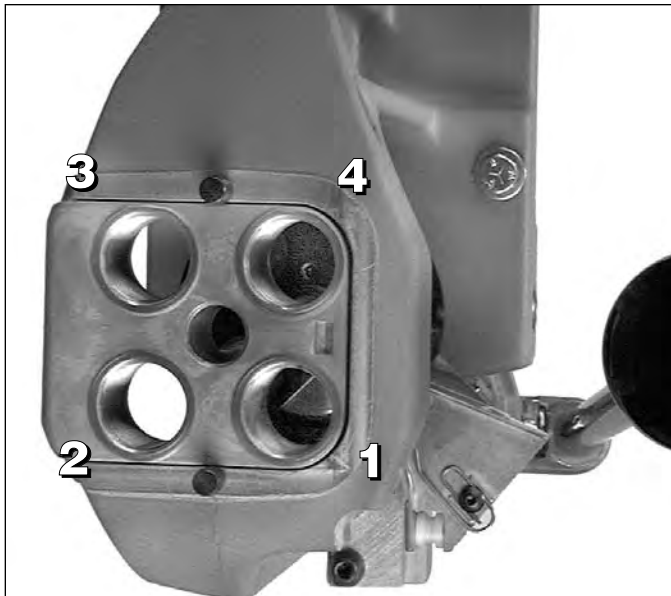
[Figure 11] Werkzeugkopf/Matrizen [toolhead/die]-Stations- Orientierung.
